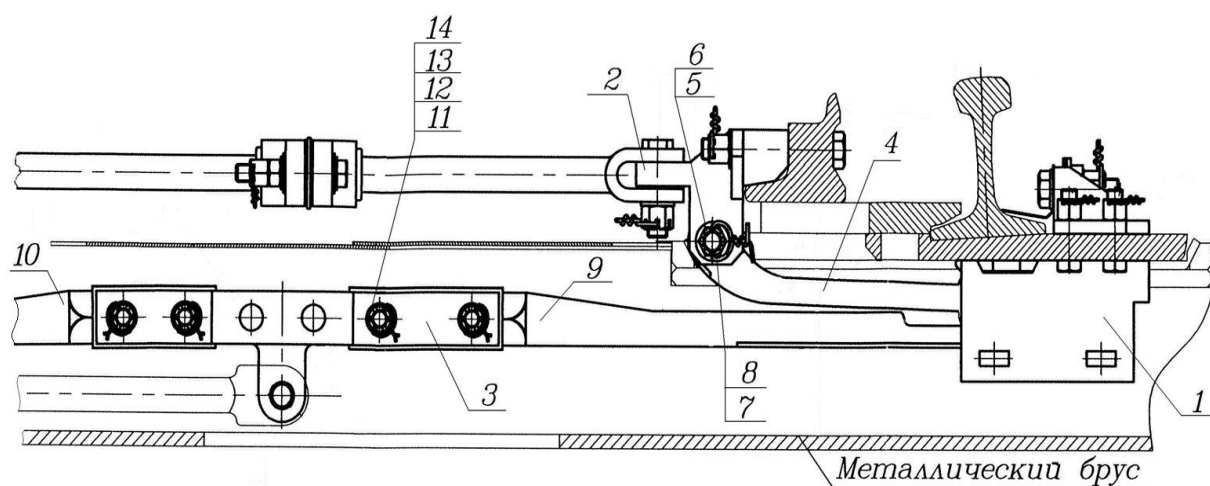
Замыкатель внешний вертикальный ВЗ-7 (черт. 17713-00-00)
